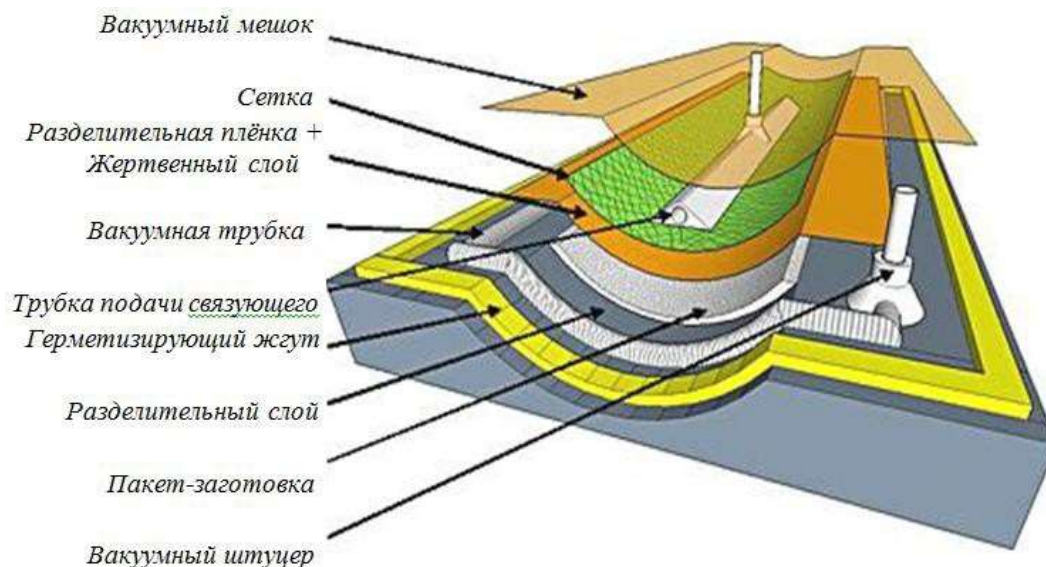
Схема сборки пакета из заготовки в виде преформы
